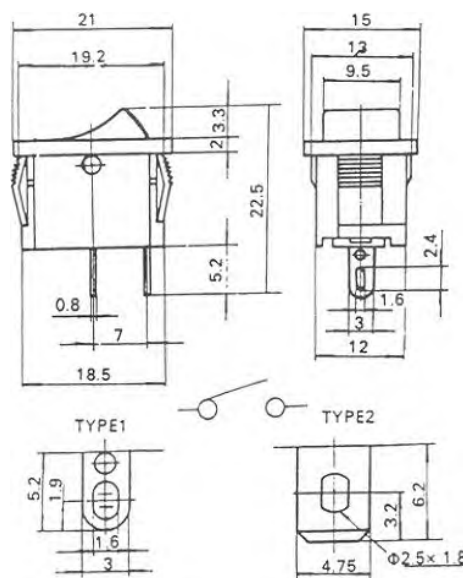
Розміри габаритні та вигляд зовнішній перемикача
